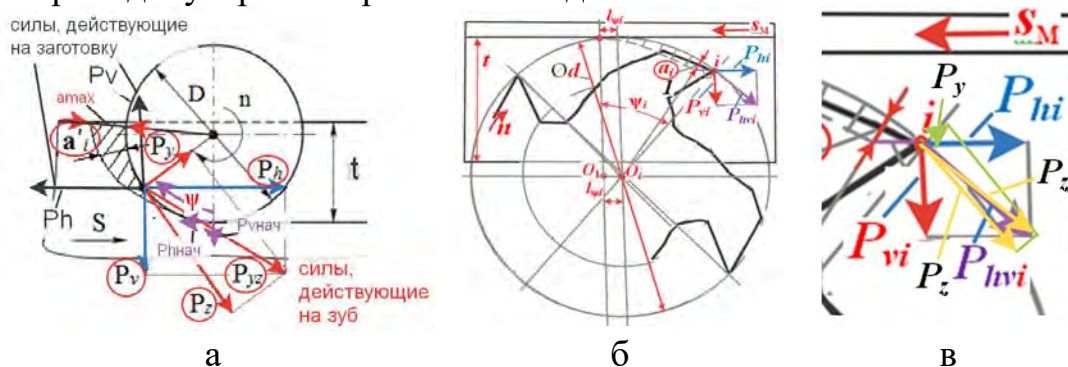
Схема направления составляющих силы резания при несимметричном встречном концевом фрезеровании: а – при положении фрезы после заготовки на виде сверху; б – при положении фрезы перед заготовкой на виде сверху, как в рассматриваемом эксперименте; в – схема действия составляющих  $P_{vi}$  и  $P_{li}$ , а также  $P_z$  и  $P_y$  и их результирующих  $P_{hvi}$  и  $P_{zy}$
